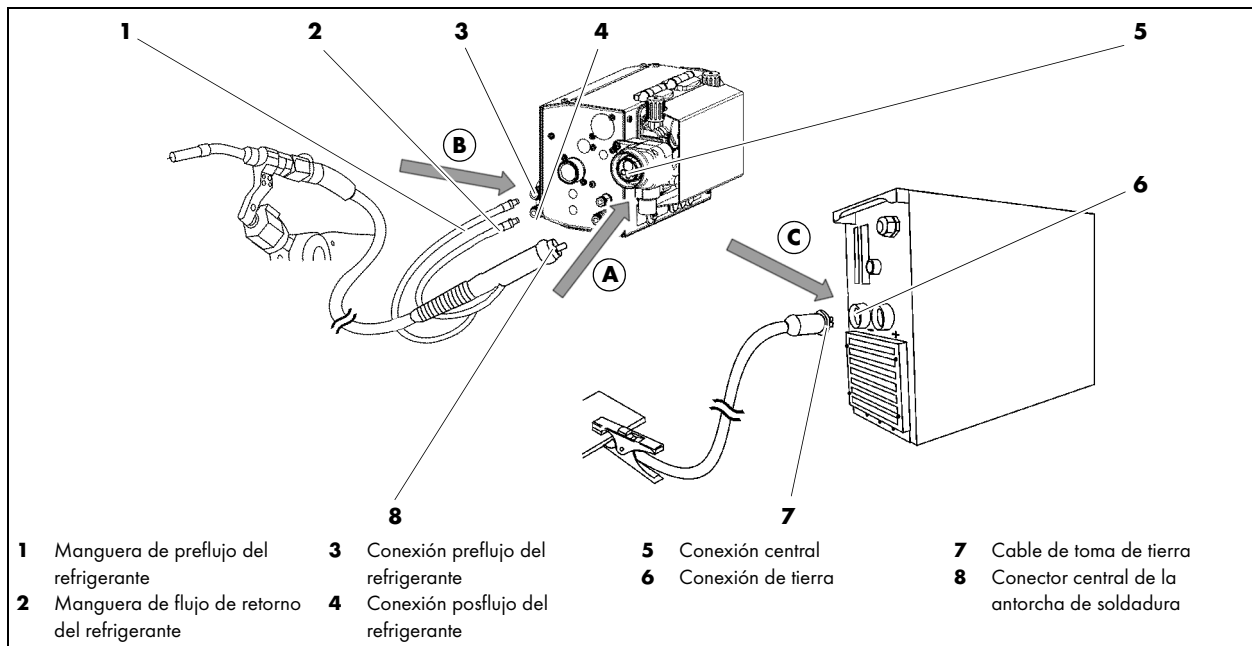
Conjunto de cables de la antorcha de soldadura (euroconector central) iROB Feed 22 (versión con devanadora o alimentador montado a la derecha)
